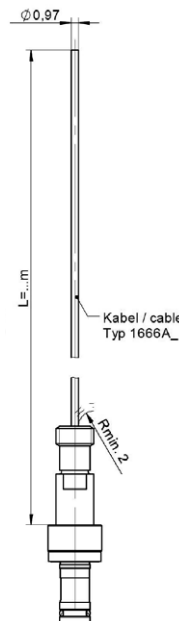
Drucksensor Typ 6177B mit Single-Wire Kabel
